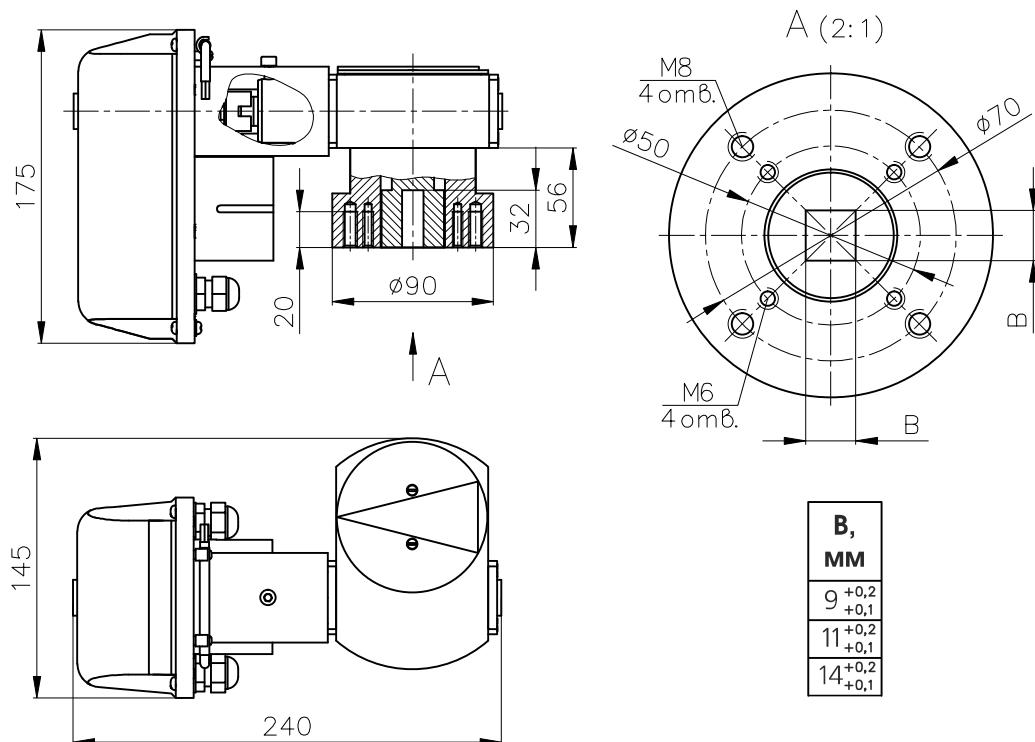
Габаритные и присоединительные размеры ЭИМ
